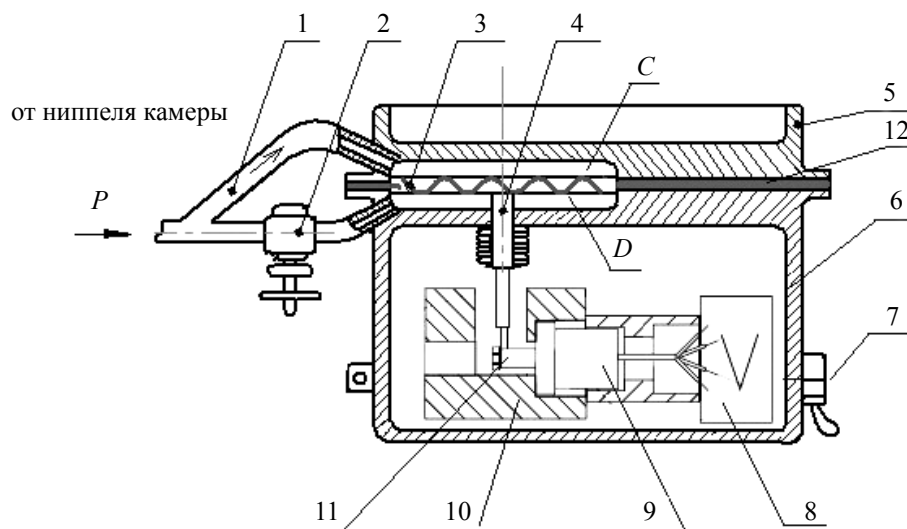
Общая принципиальная схема электронного прибора для исследования гистерезисных потерь в пневматической шине: 1 – воздухопровод; 2 – вентиль; 3 – измерительная мембрана; 4 – шток; 5 – фланец; 6 – корпус прибора; 7 – разъем крепления крышки и корпуса; 8 – блок электронного преобразователя; 9 – корпус рычажного тензопреобразователя; 10 – корпус сенсорного блока датчика; 11 – рычажный механизм; 12 – резиновая прокладка
